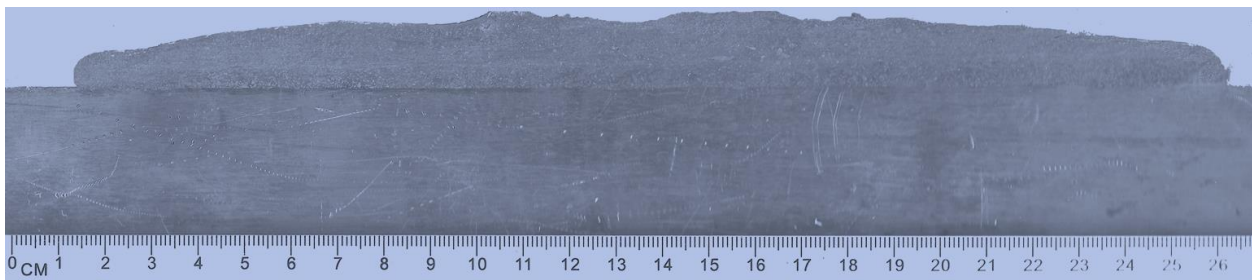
Зразок, наплавлений багатовалковим наплавленням з використанням порошкових стрічок
